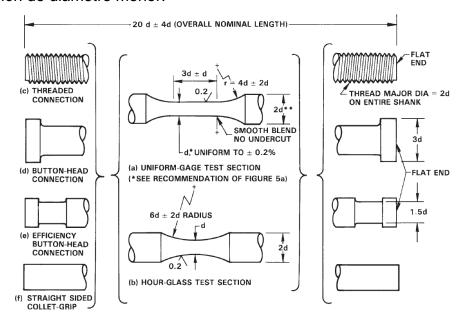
Probetas para ensayos de fatiga axial Fuente: ASTM E606-92 (2004)
